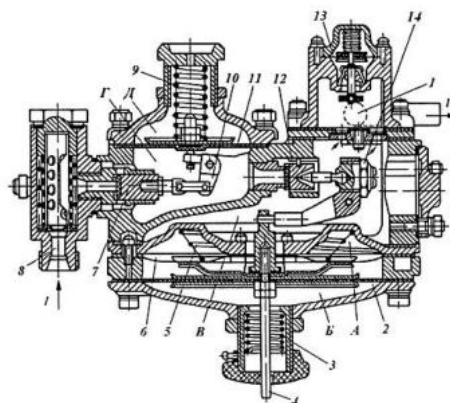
Двухступенчатый газовый редуктор низкого давления
